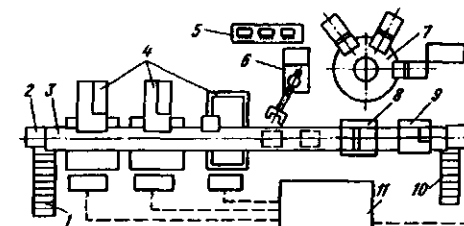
Гибкая автоматизированная линия с последовательным выполнением операций: 1 – конвейер подачи заготовок на линию; 2 – автоматический загрузчик линии; 3 – шаговой конвейер; 4 – станки с ЧПУ; 5 – накопитель шпиндельных головок; 6 – промышленный робот; 7 – станок с ЧПУ с многошпиндельными головками; 8 – установка для удаления стружки и мойки деталей; 9 – контрольно-измерительная машина; 10 – конвейер с обработанными деталями; 11 – ЭВМ линии
